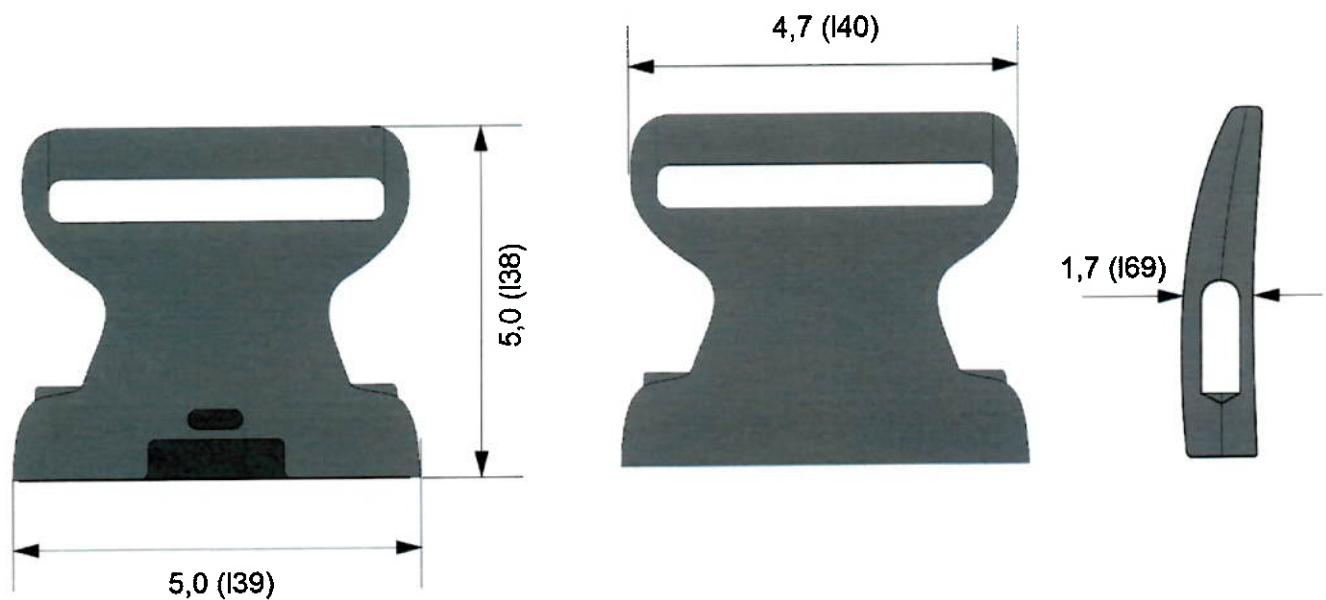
Detalhes da presilha de encaixe tipo fêmea
